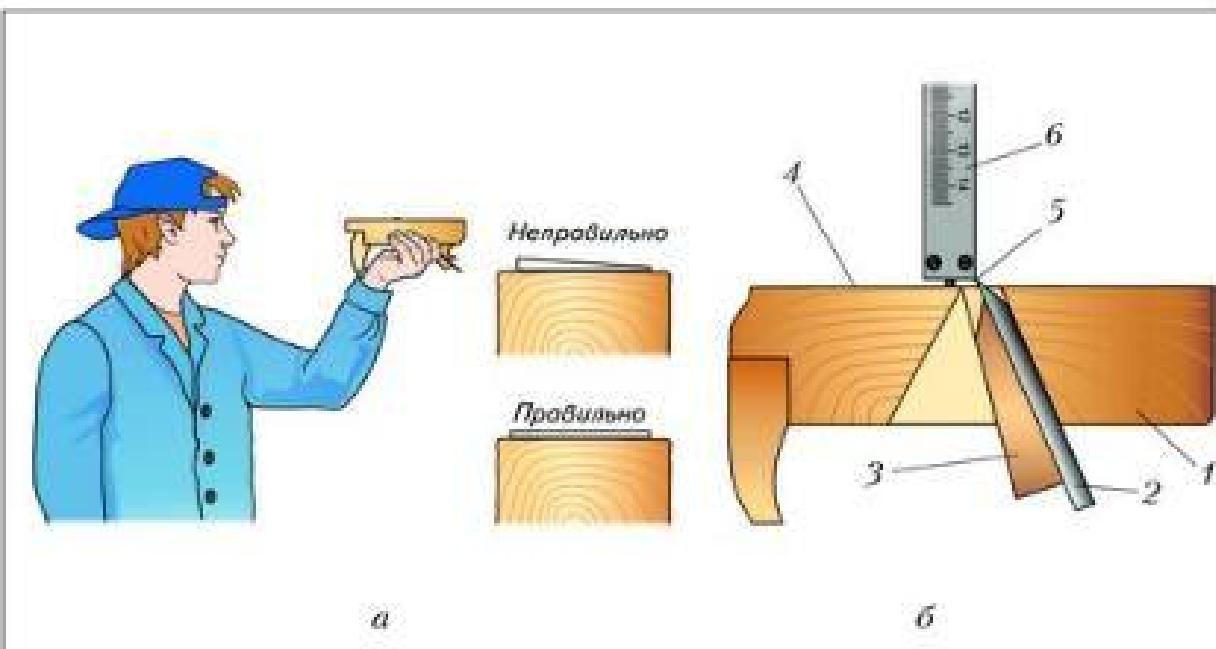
Настройка рубанка: *а* – оценка положения режущей кромки; *б* – измерение расстояния от подошвы до режущей кромки: 1 – колодка; 2 – нож; 3 – клин; 4 – подошва; 5 – режущая кромка; 6 – штангенциркуль
